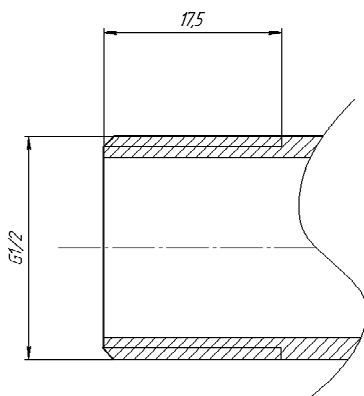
Присоединительные размеры патрубка рубашки обогрева
